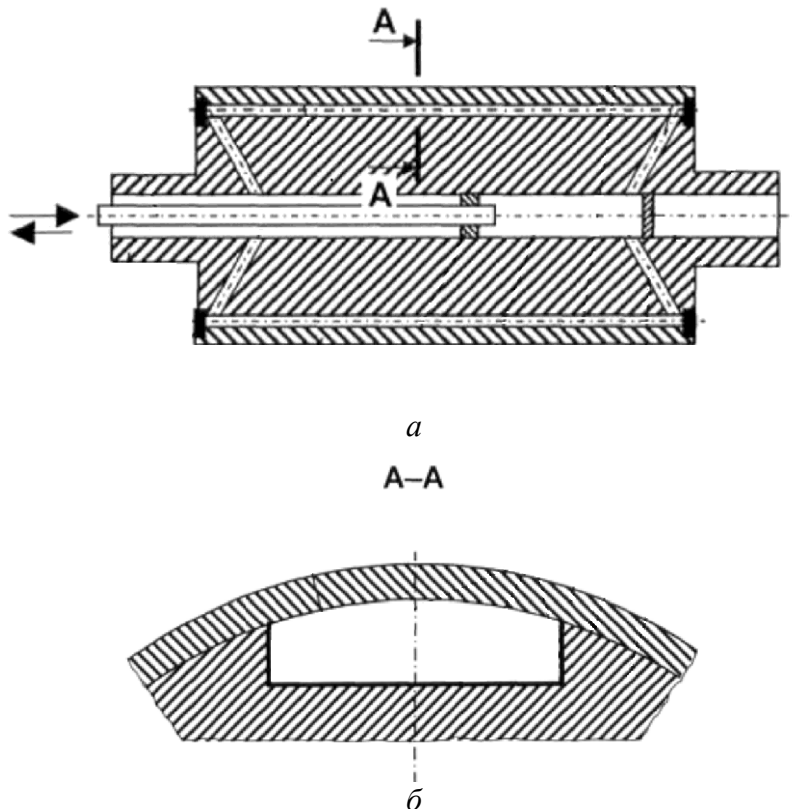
Фрезеровані охолоджувальні канали: *а* – поздовжній переріз валка; *б* – розріз А-А
